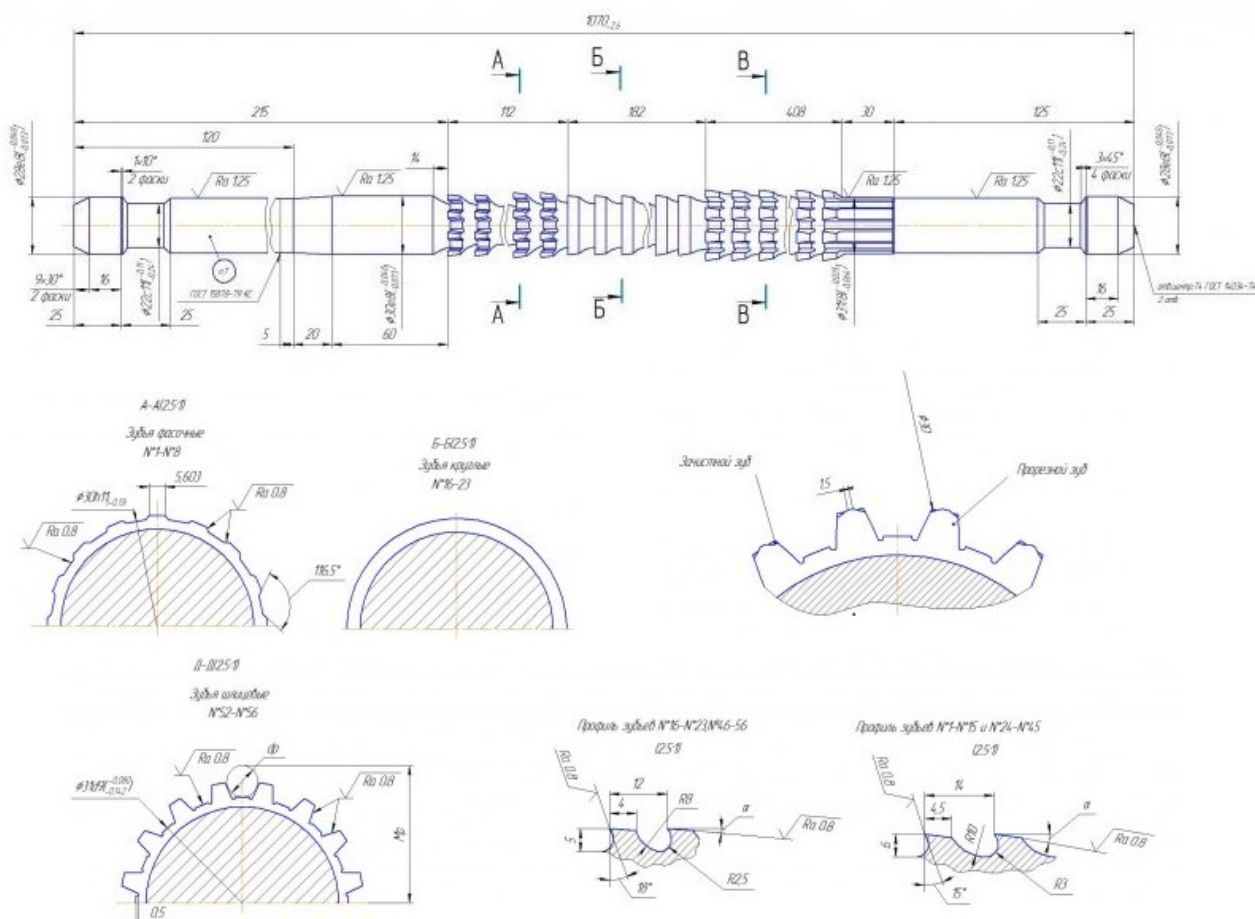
Фрагмент рабочего чертежа шлицевой эвольвентной протяжки
